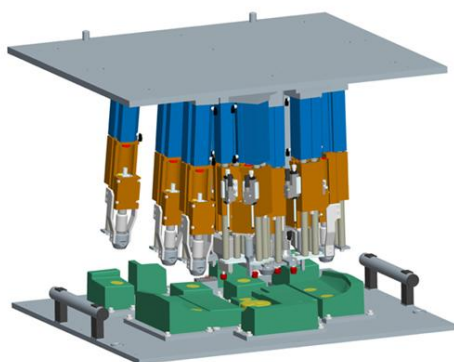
Многоточечный автоматизированный комплекс для ультразвуковой сварки фирмы Herrmann Ultrasonic
